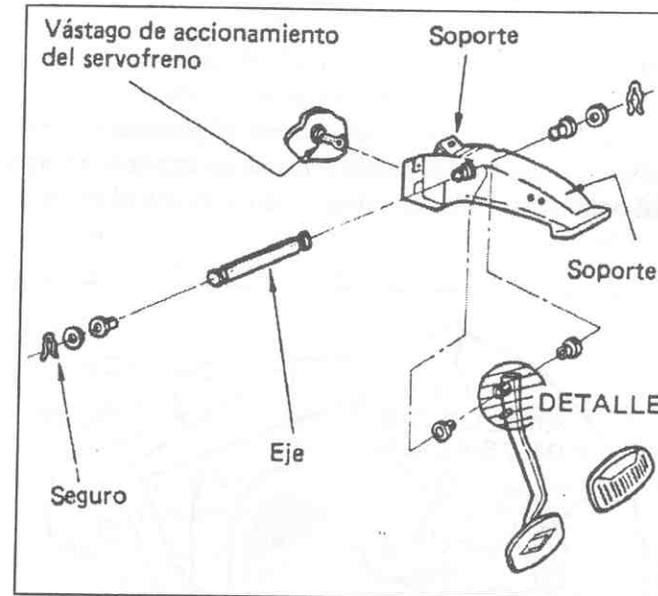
Despiece del pedal de freno de unidad con caja automática.
